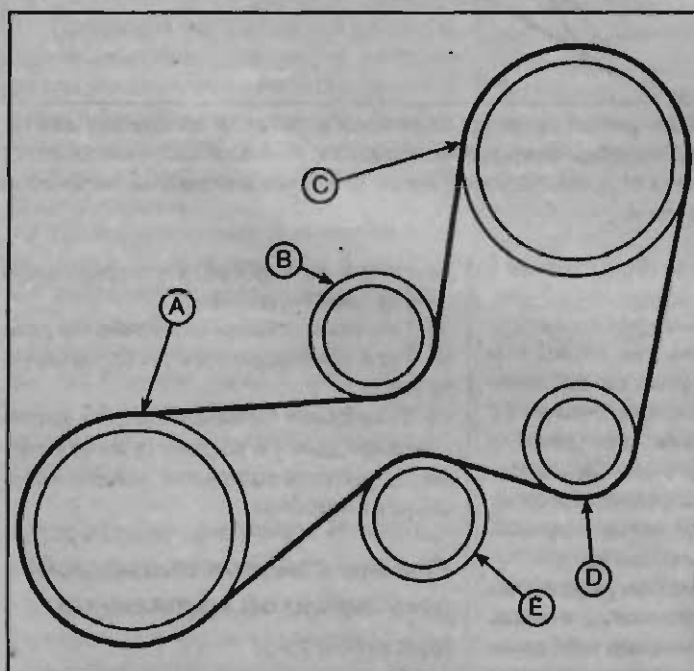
Расположение ремня привода навесных агрегатов на шкивах двигателя 1,8 л без системы кондиционирования воздуха: А – шкив коленчатого вала; В – шкив автоматического механизма натяжения ремня; С – шкив насоса усилителя рулевого управления; D – шкив генератора; E – направляющий шкив
